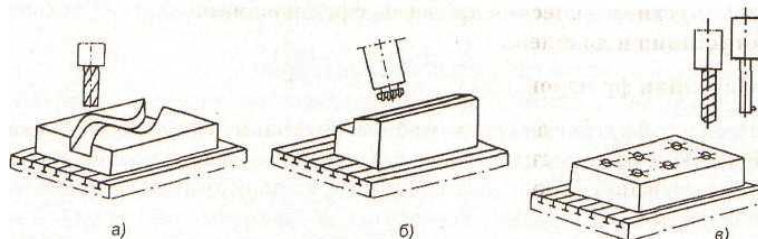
Схемы обработки заготовок на продольно-фрезерных станках
